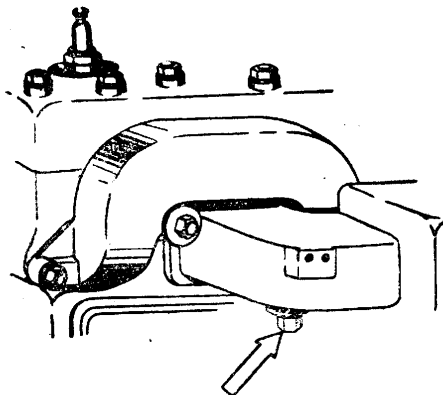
Место пробки для слива бензина из впускной трубы двигателя.
